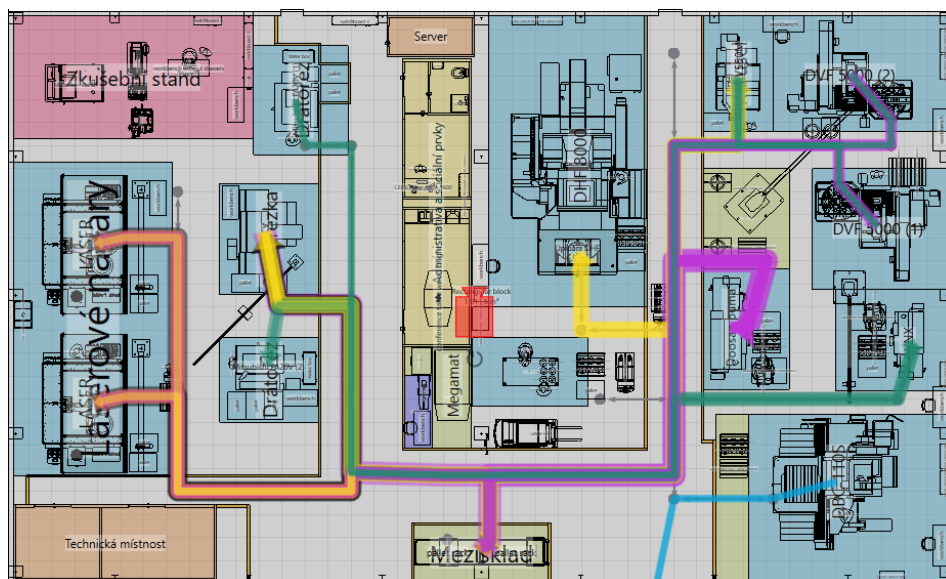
Technologický layout Chotikov - SW Solid edge
